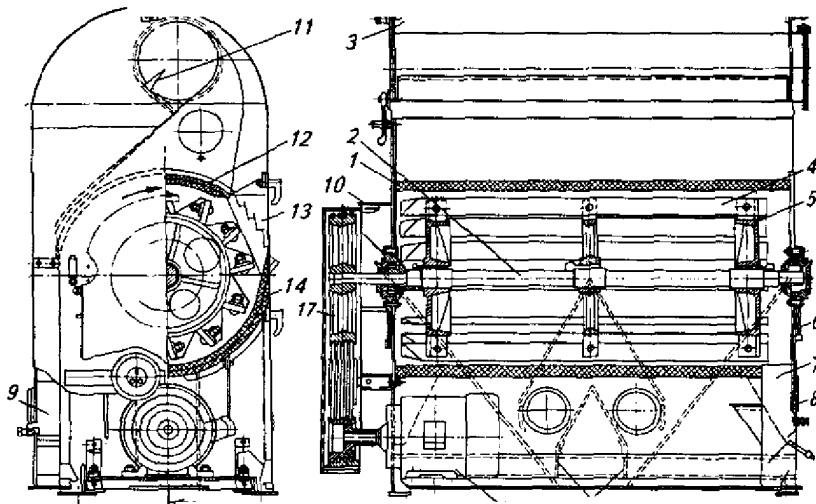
Общий вид обочной машины ЗНМ-5;
